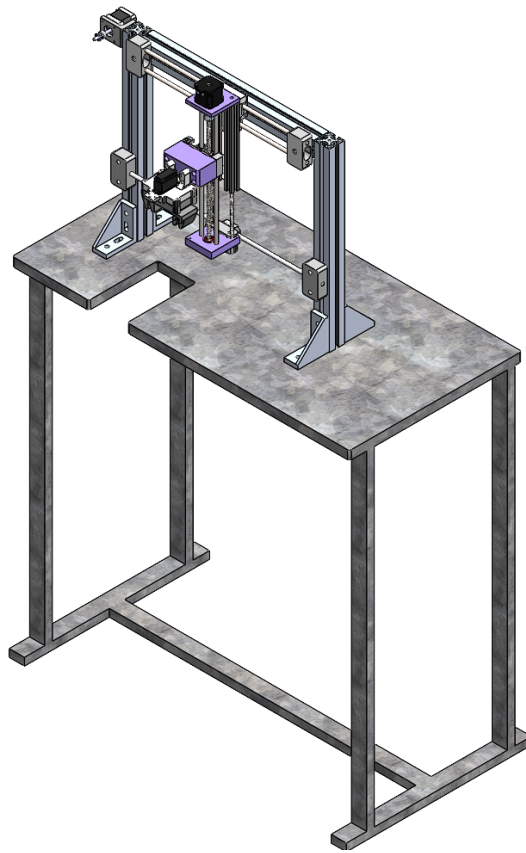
Vista Isométrica del Ensamblaje. Fuente: Autores
